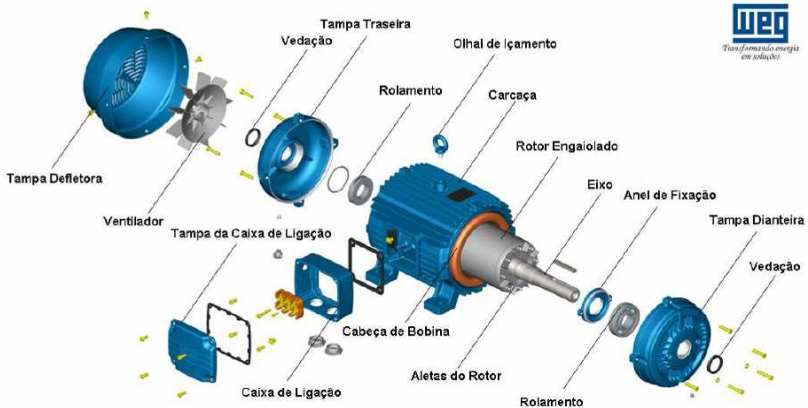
Principais componentes de um motor elétrico trifásico.
